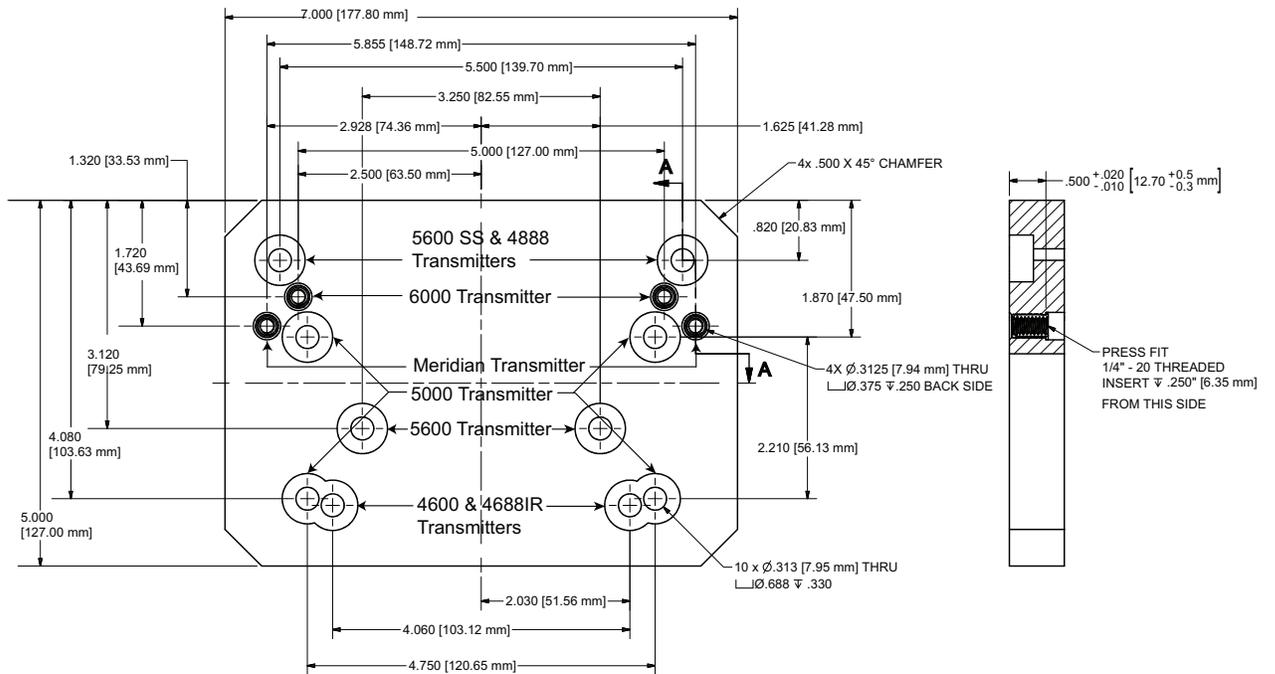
Dimensiones de la placa de montaje de adaptación – HDPE
